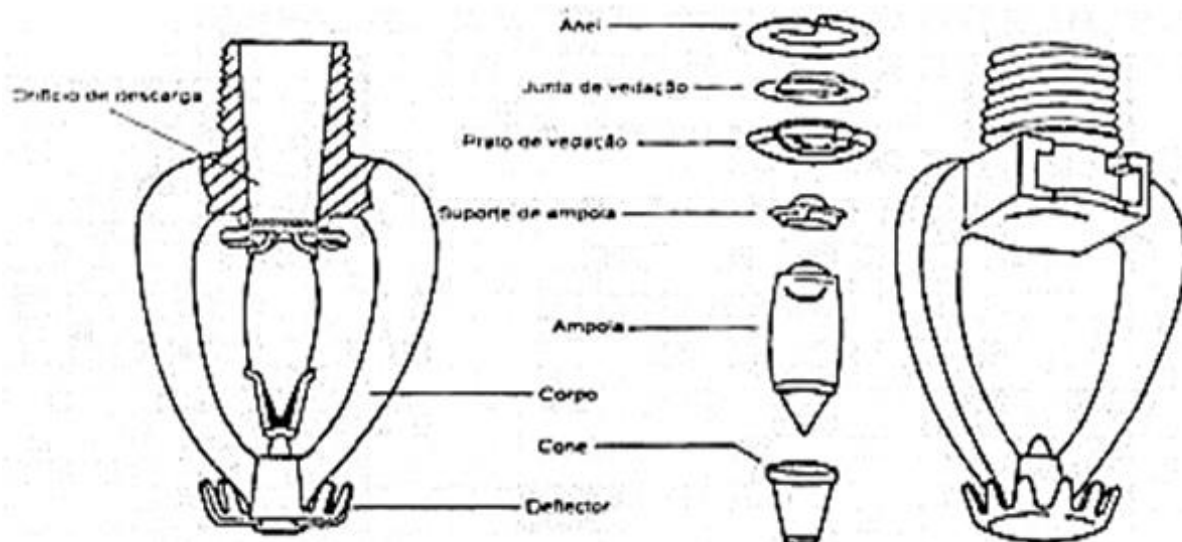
Esquema da estrutura interna de um sprinkler;
